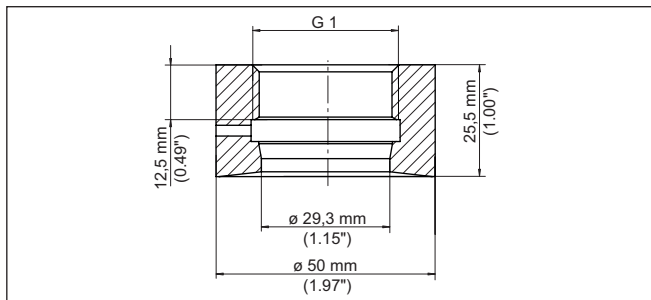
Dimensiones racor para soldar directo G1 (ISO 228-1) - Junta tórica
